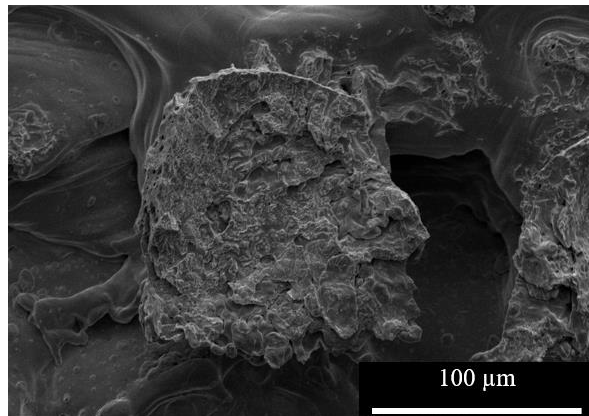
Zoom sur une des zones d'arrachement de soudure sur le contact fixe avec un grossissement X600
